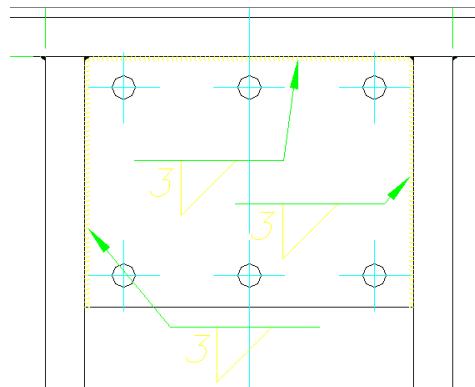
Soldadura que une la placa con los perfiles angulares de la estructura base
